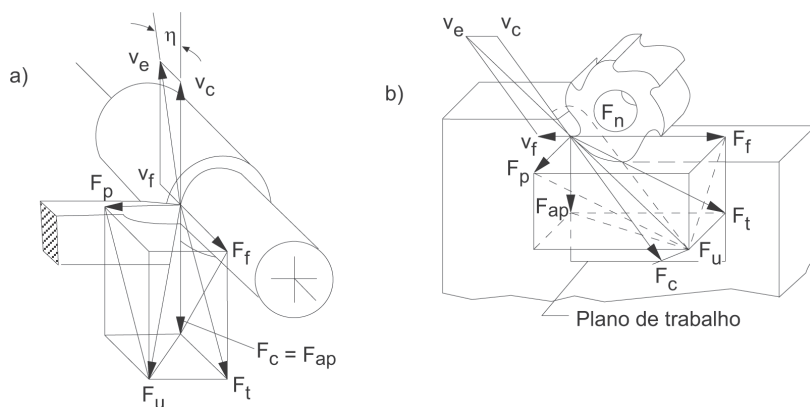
Componentes da força de usinagem: a) torneamento e b) fresamento
